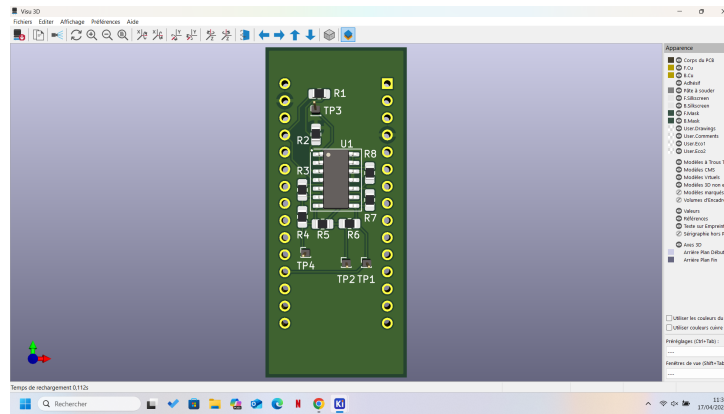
Vue de dessous du PCB réalisé avec Kicad
